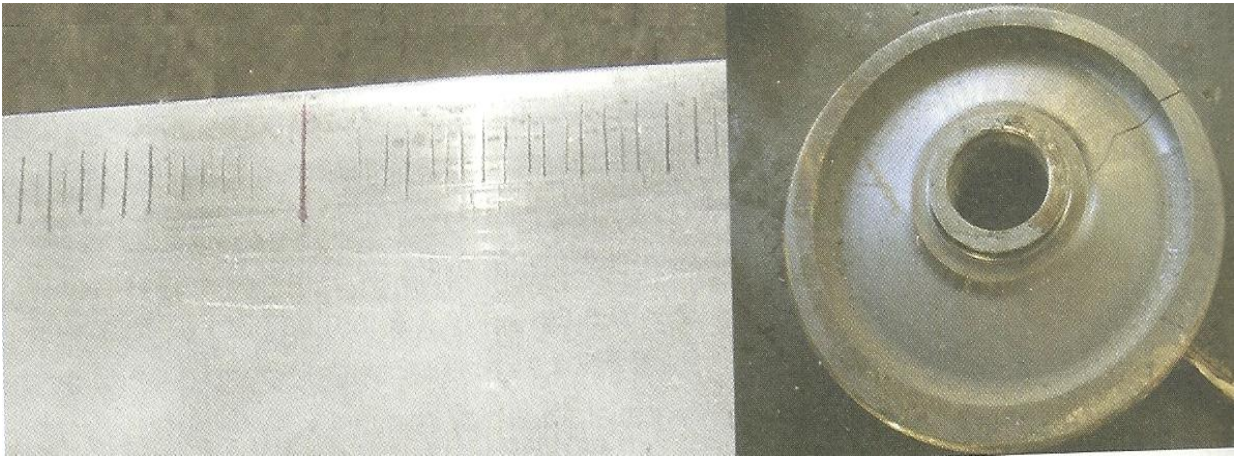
Parte de uma roda com defeito causado por trincas térmicas [MINICUCCI, 2011].
